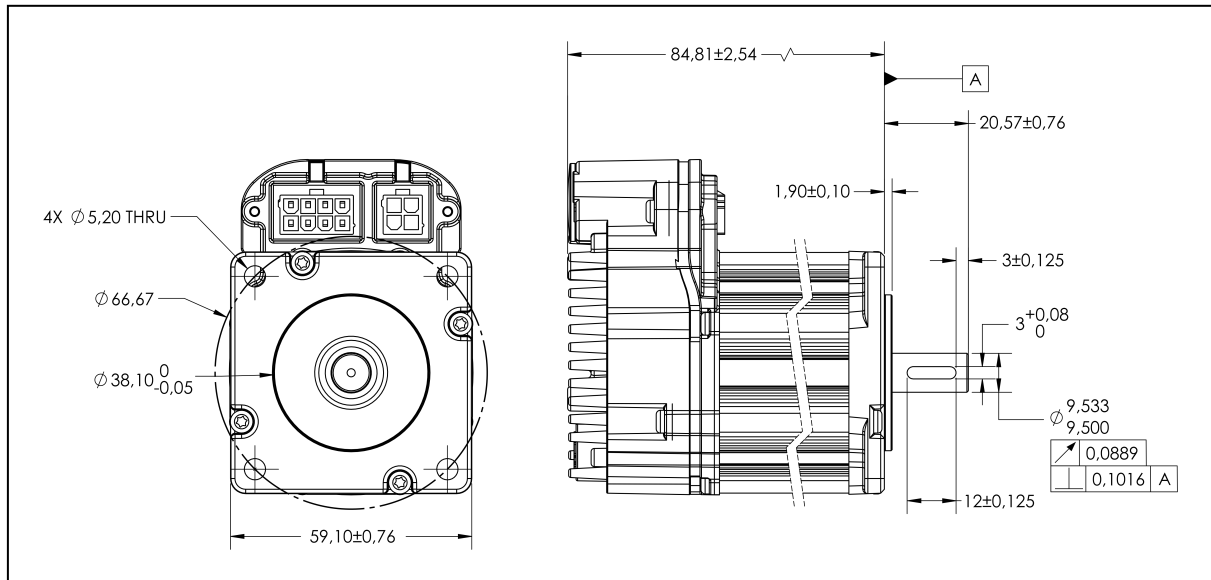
Dimensões em mm do motor selecionado para os estágios lineares. Adaptado de Teknic (2020b) para destacar as dimensões-chave do motor.
